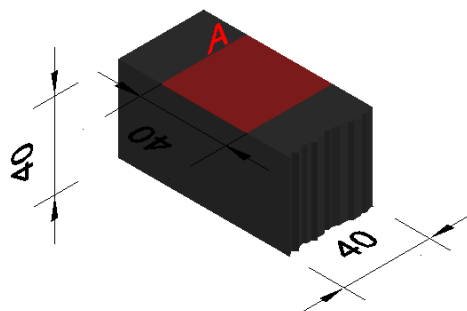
Área de aplicação da carga (dimensões em mm).
